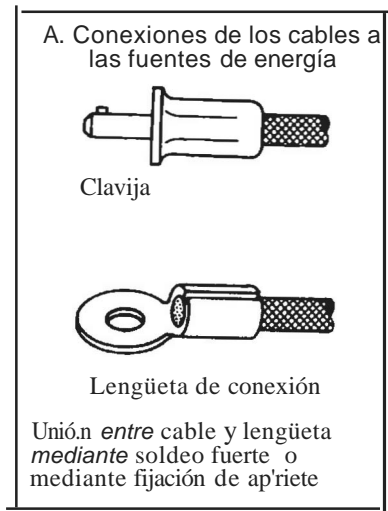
CONEXIONES PARA CABLES DE SOLDEO
